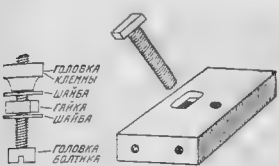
Подготовка клеммы и эбонитовой пластинки для монтажа статора.
